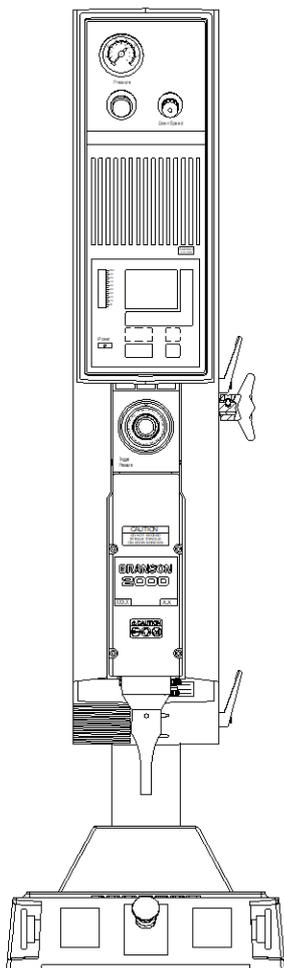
Sistema de soldadura compacto 2000IW+
